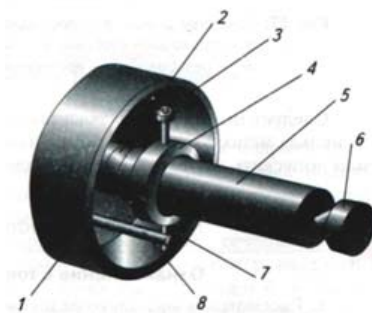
Установка заготовки при помощи поводковой планшайбы:
